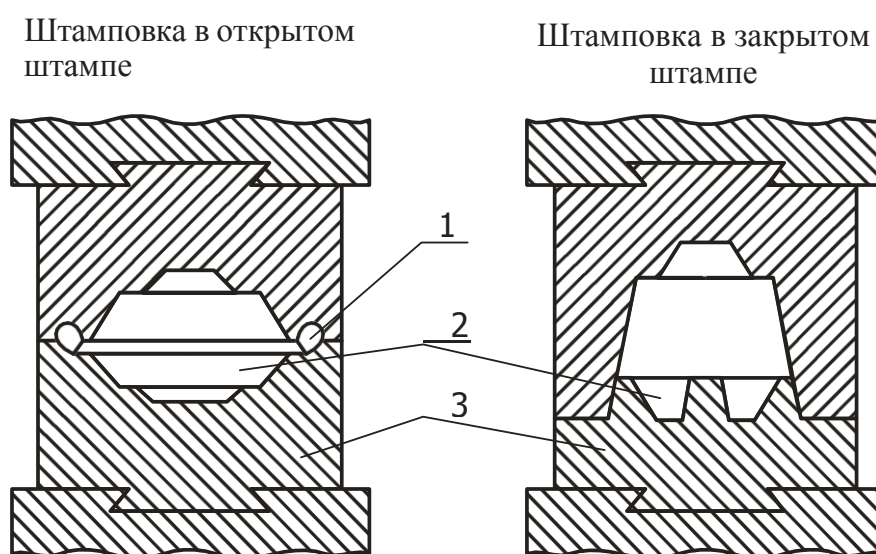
Схема штамповки и получаемые изделия: 1 – облойная канавка; 2 – заготовка; 3 – штамп.
